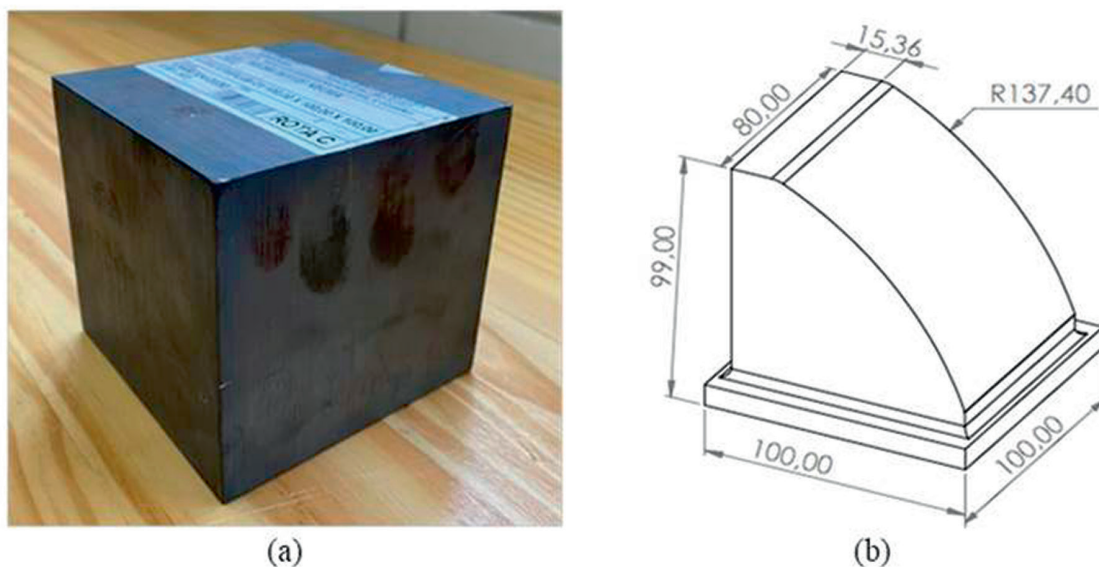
(a) Exemplo de bloco para confecção dos corpos de prova e (b) superfície final a ser obtida.
